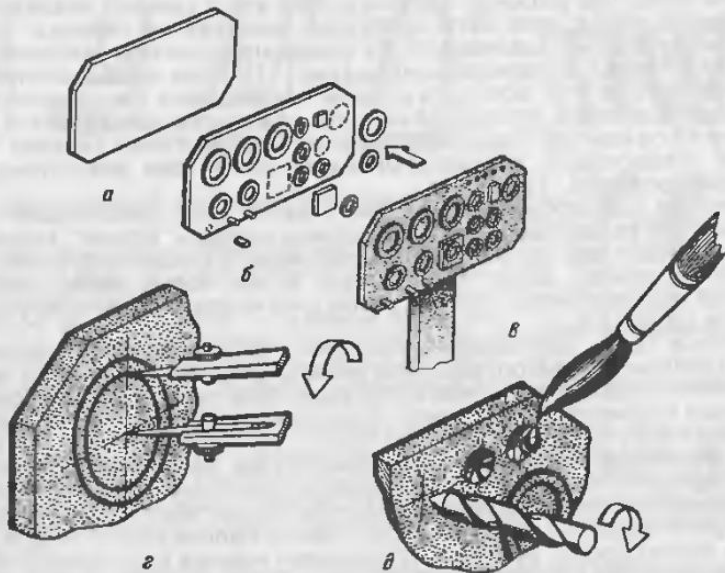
Изготовление приборной доски с выступающими ободками приборов: а - заготовка доски; б - наклейка колечек, ободков, мелких пультов; в - доска в сборе, на державке, произведена задувка краской; г - разметка приборных шкал; д - имитация цветных точек
